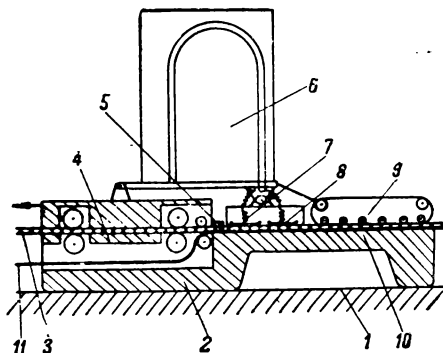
Схематическое устройство самоходного сварочного агрегата
